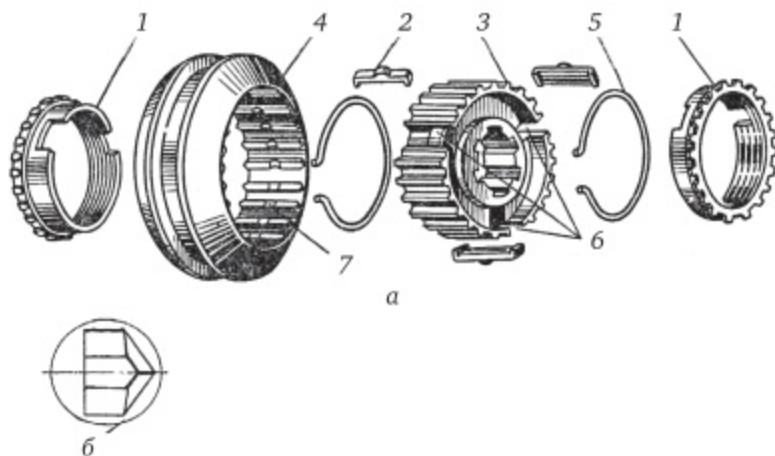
Детали синхронизатора с блокирующим зубчатым венцом и толкающими сухарями:
